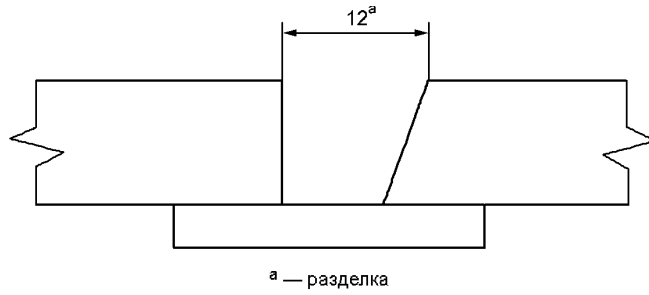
Комбинированный контрольный образец с FW/BW
